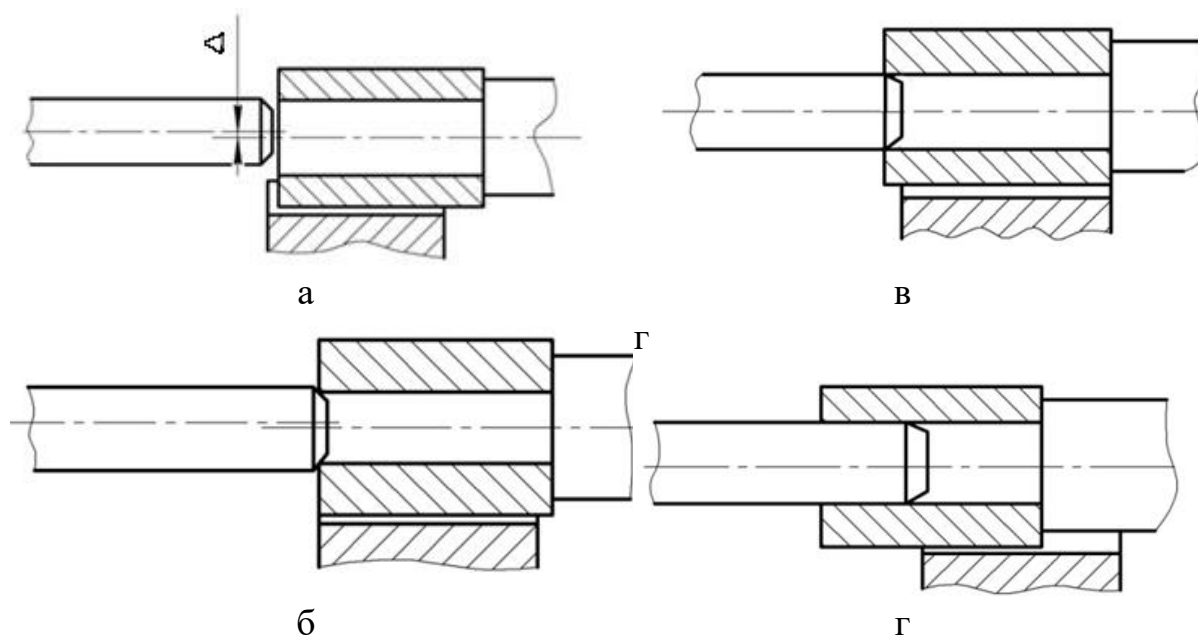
Схема процесса смены баз при сопряжении по цилиндрическим поверхностям
